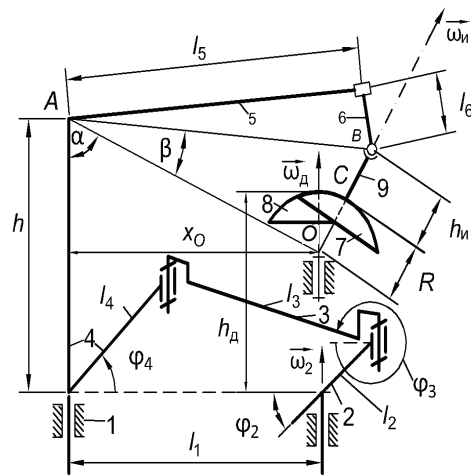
Размерная цепь рабочей зоны станка модели ШП при обработке деталей с неполными сферическими поверхностями: 1 – основание; 2 – кривошип; 3 – шатун; 4 – рычаг со стойкой; 5 – штанга; 6 – поводок; 7 – инструмент; 8 – деталь; 9 – хвостовик инструмента
